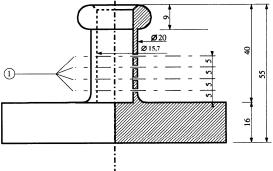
Полый бронзовый цилиндр, закрытый с одной стороны; чертеж и размеры детали в мм
